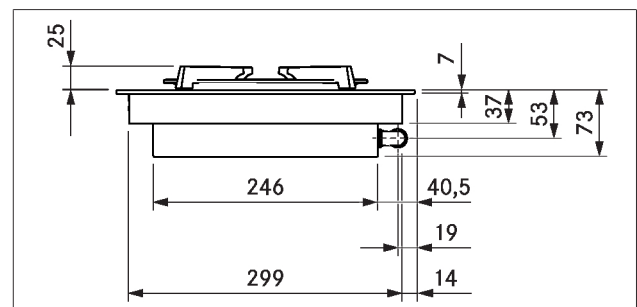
Dimensões do aparelho CKG, vista frontal
